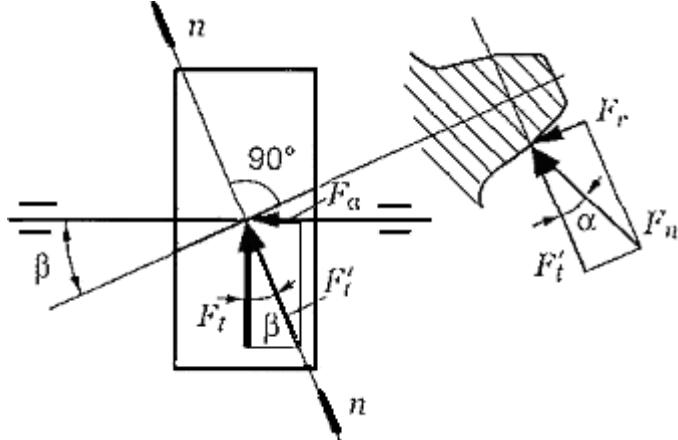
Схема действия сил в зацеплении косозубых колес
